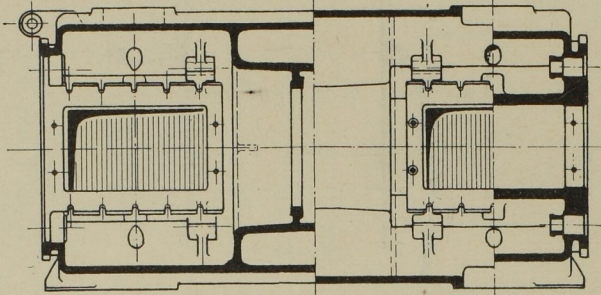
Längsschnitt und Grundriss. Masst. 1:40.
